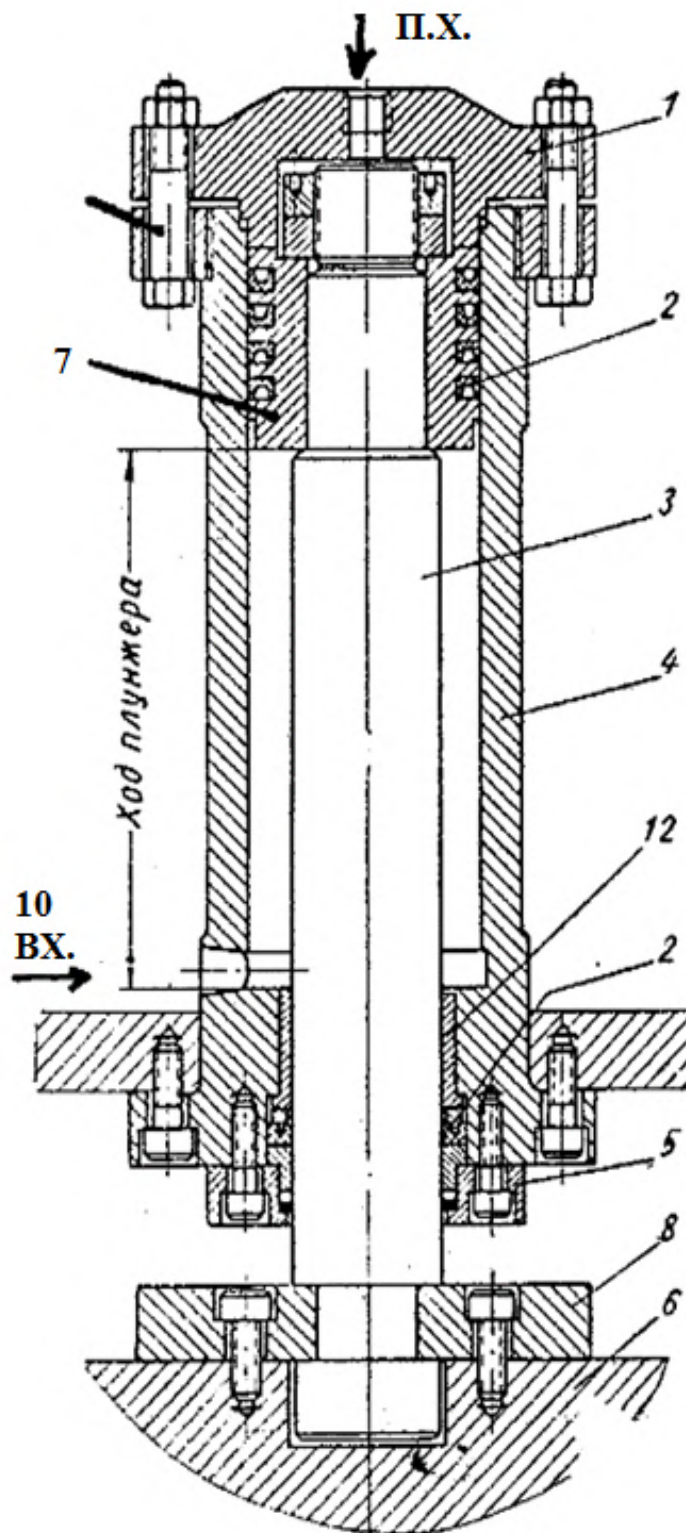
Главный гидроцилиндр рамного пресса:
